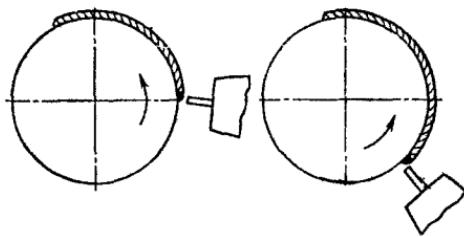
Схемы расположения электрода при сварке в CO_2 поворотных кольцевых швов на весу
